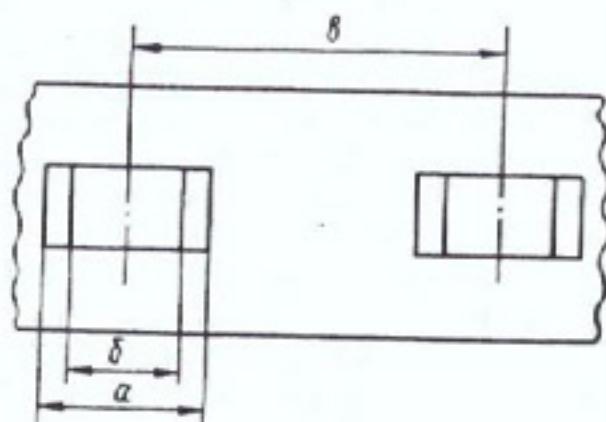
Разметка гнезд с наклонными стенками (вид сверху).
